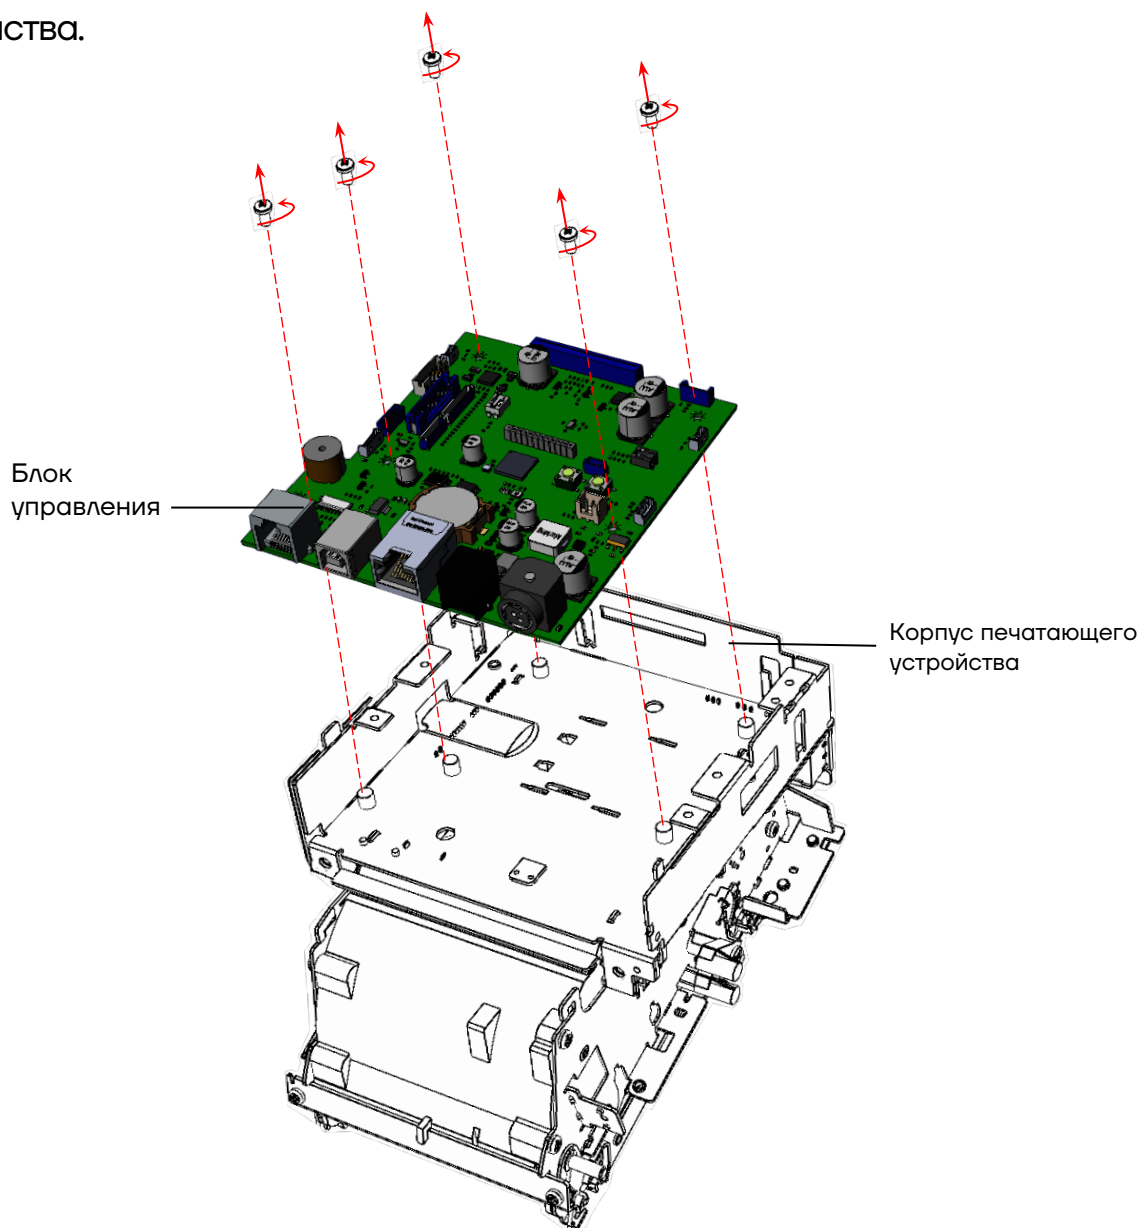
Отделение блока управления от корпуса печатающего устройства
